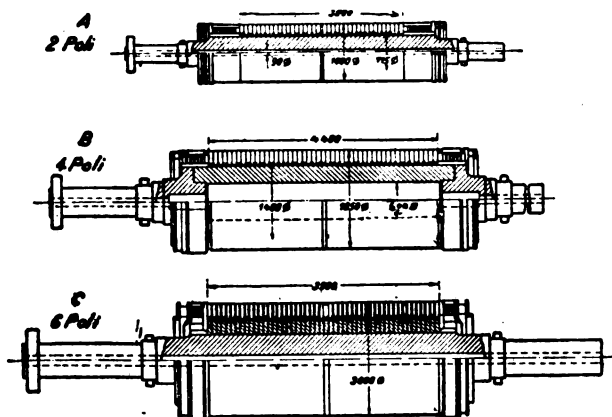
Tipi di rotor per macchine a 2-4-6 poli.
